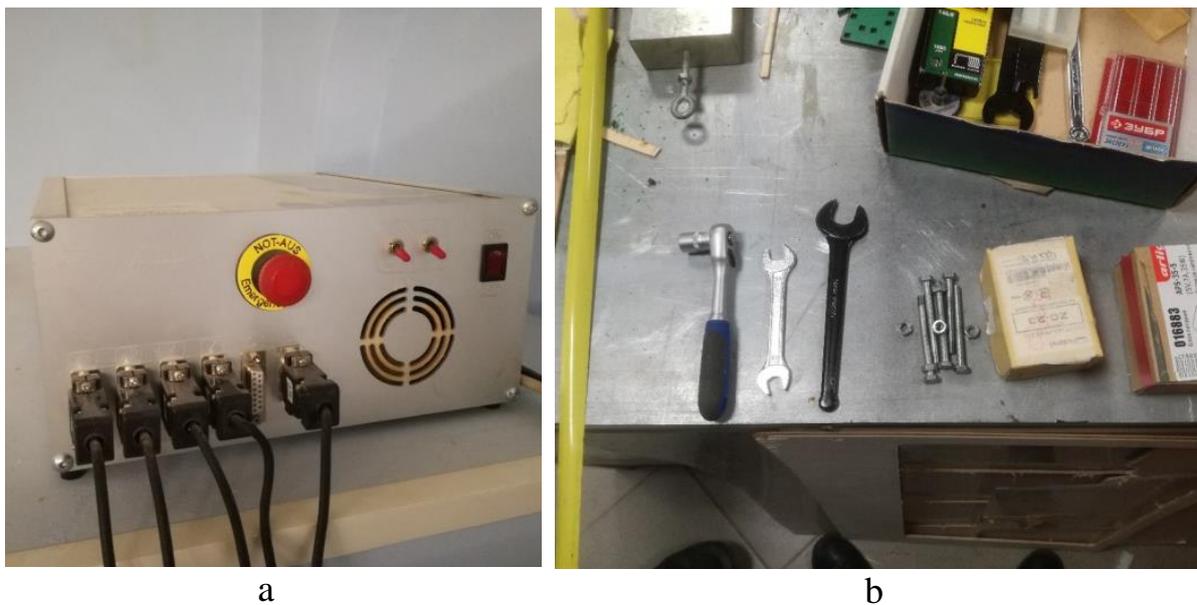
Блок управления фрезерным станком (а) и набор для работы с фрезерным станком HIGH-Z S-1400 (b).
